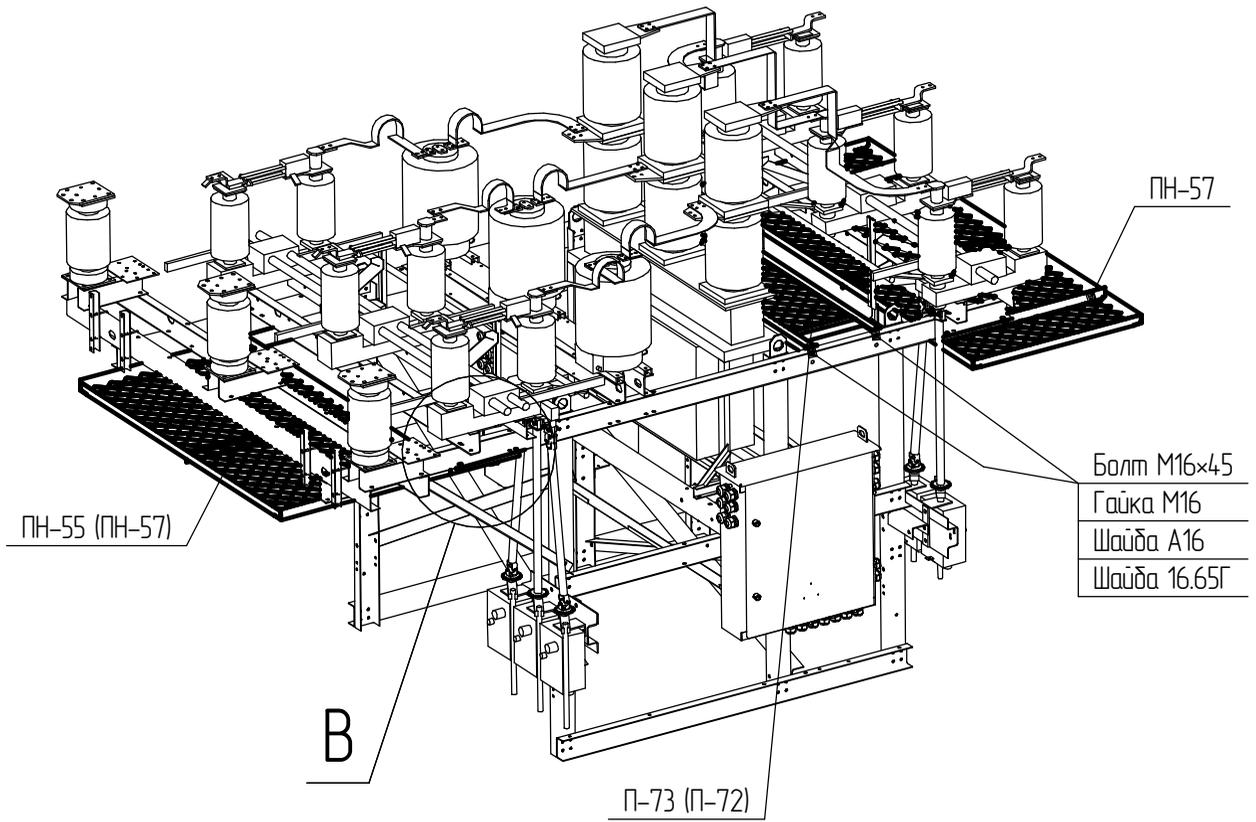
Установка на блок выключателя 35 кВ защитного козырька над приводами разъединителя
